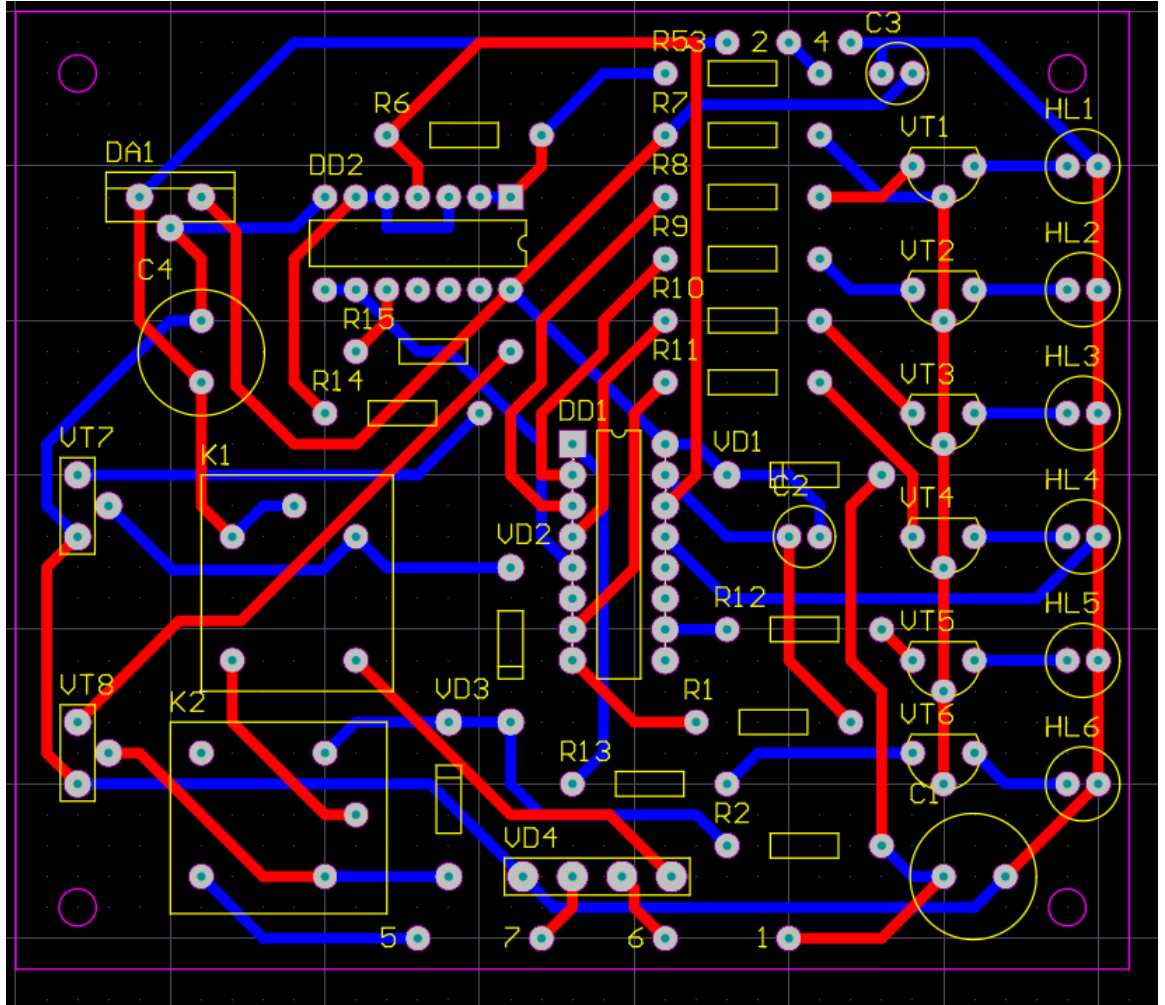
Плата друкована виготовлена в Altium Designer
